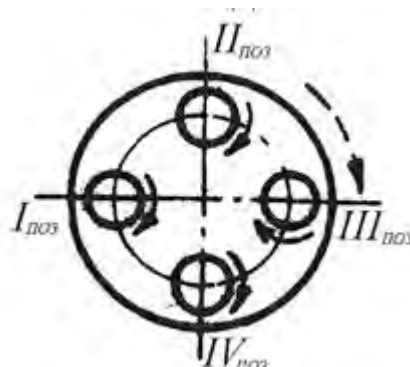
Позиції, які займаються по черзі заготовкою при обробленні на 4-шпіндельному токарному напівавтоматі
